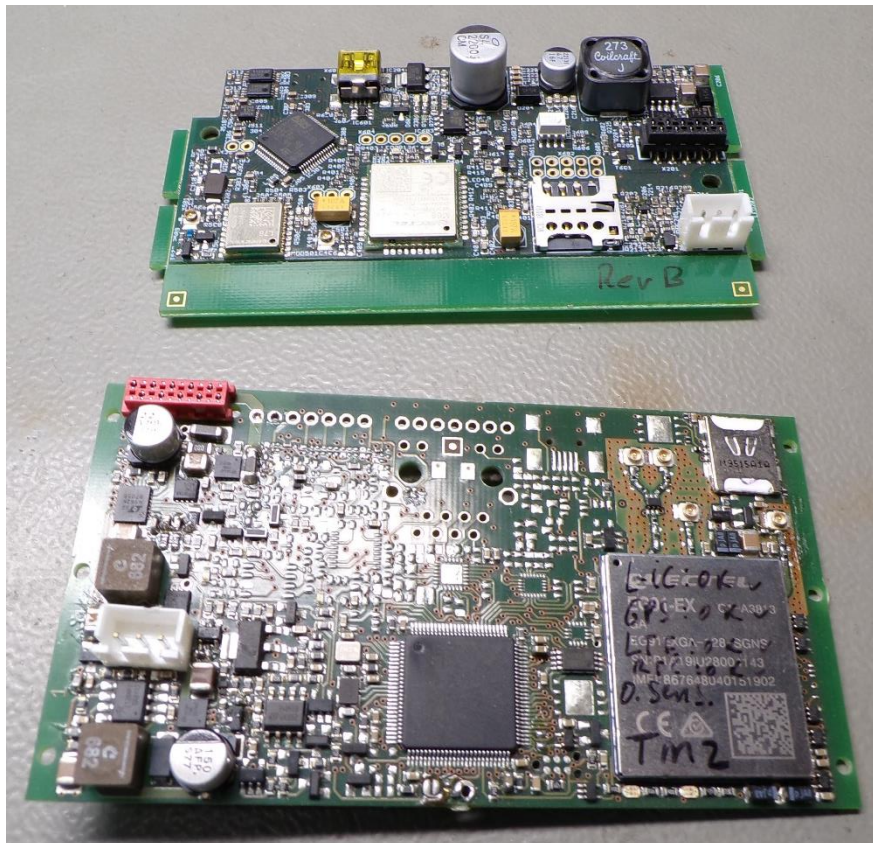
Oben PCB mit getrennten Modulen / Unten PCB mit Kombimodul
